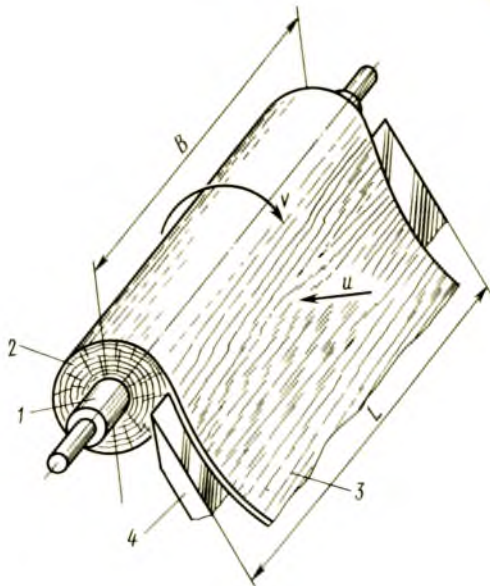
Схема получения лущеного шпона: B — длина чурака, L — длина ножа; 1 — кулачок, 2 — чурак, 3 — шпон, 4 — нож
